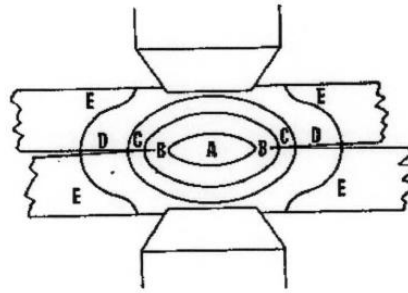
Estado Térmico de um Ponto de Soldadura após Interrupção do Fornecimento de Corrente de Soldadura [31].
